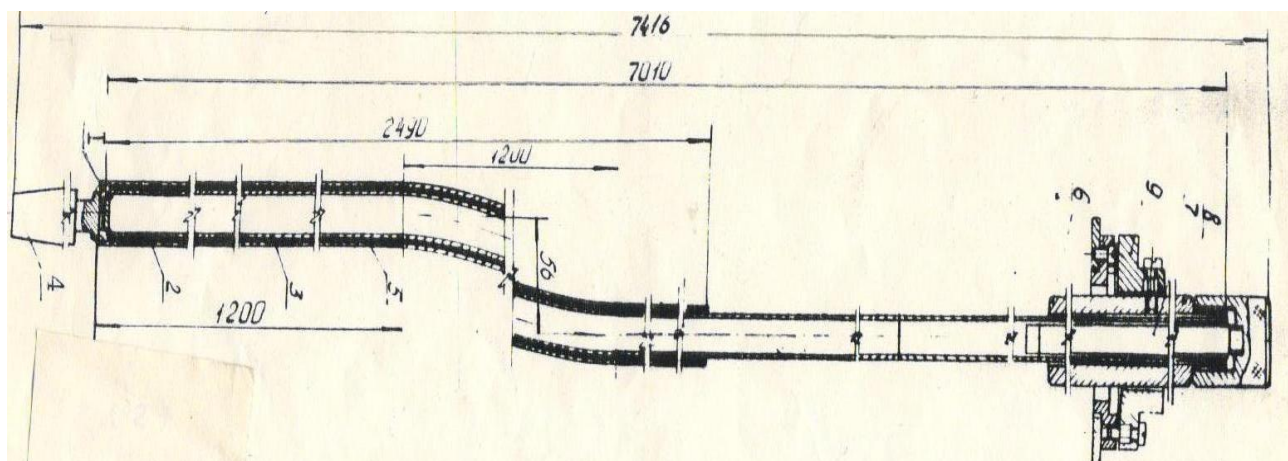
Схема канала с кадмиевым экраном: 1 – канал, 2 – чехол, 3 – экран из металлического кадмия, 4 – втулка для установления канала в сборке, 5 – внешний чехол, 6 – крепление к крышке бака реактора и 7 – приспособление для подвешивания образцов.
